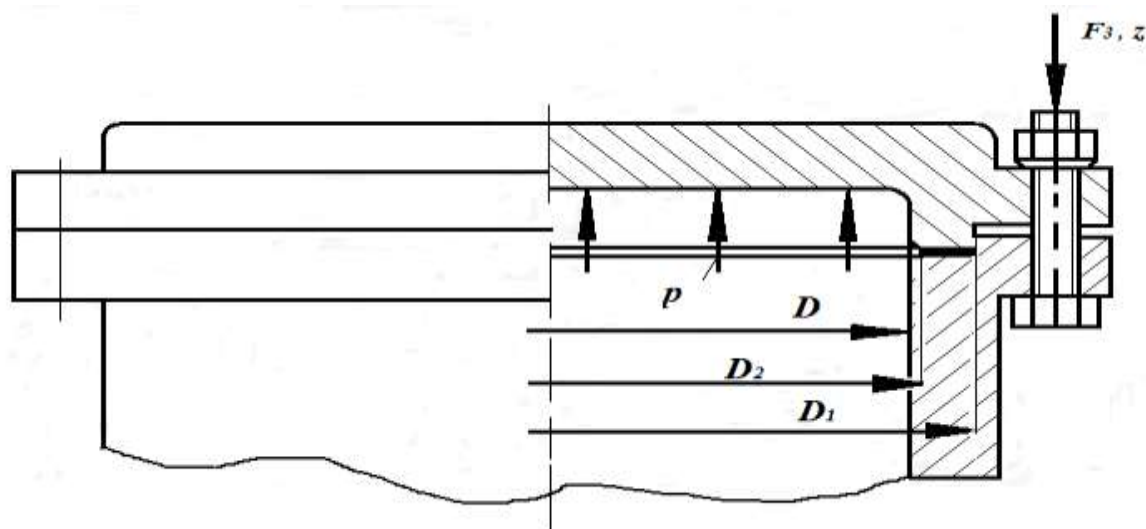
Резьбовое соединение цилиндр-крышка
